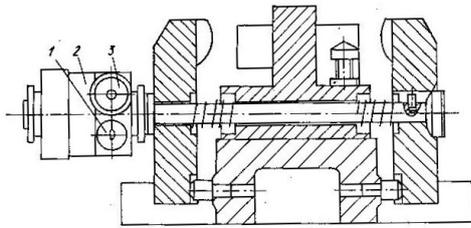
Механизированное УСП для фрезерования плоскости А и сверлении 6 отверстий на станке ЧПУ
